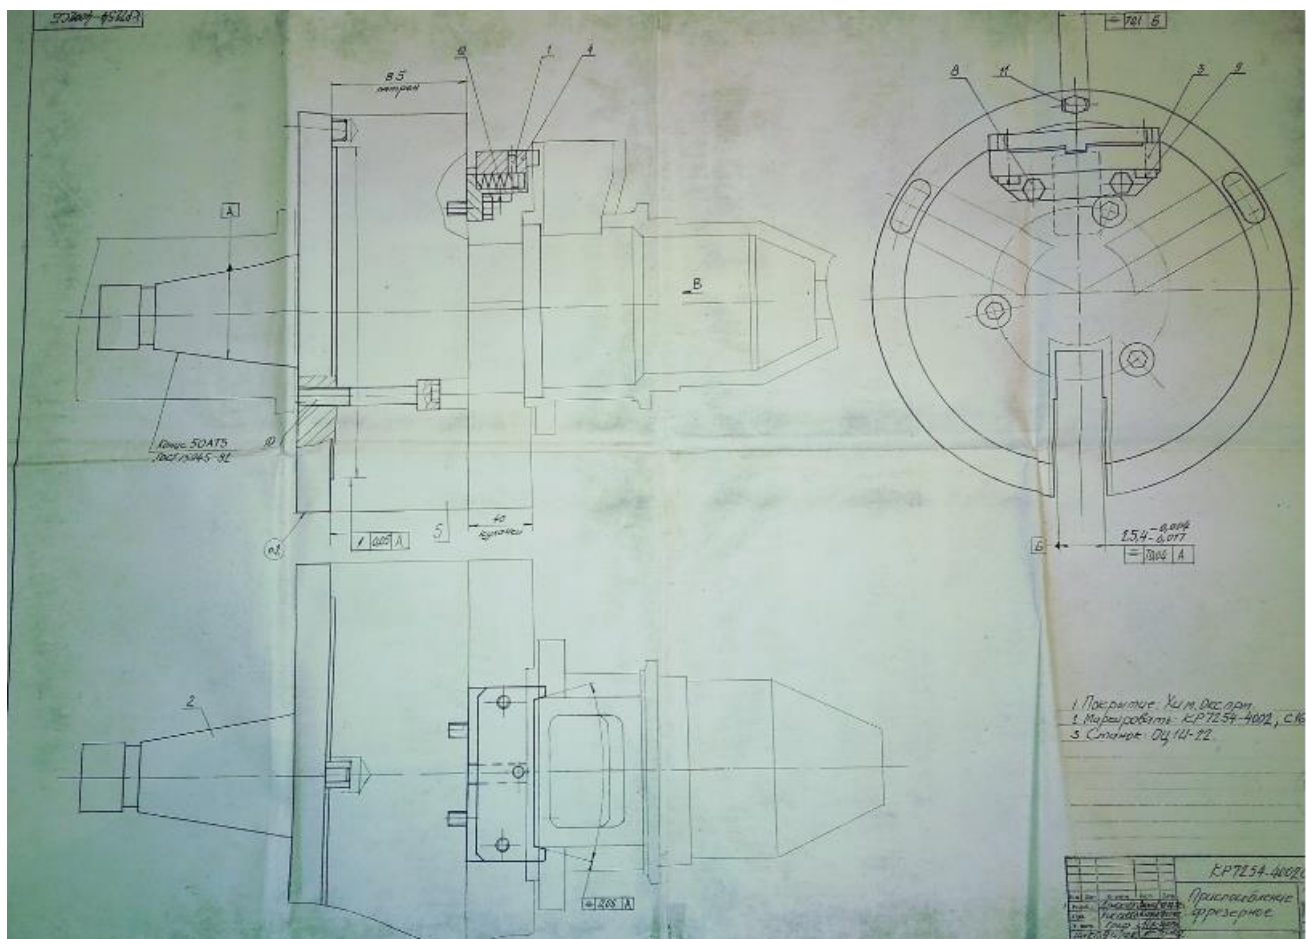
Фрезерно-сверлильное приспособление
